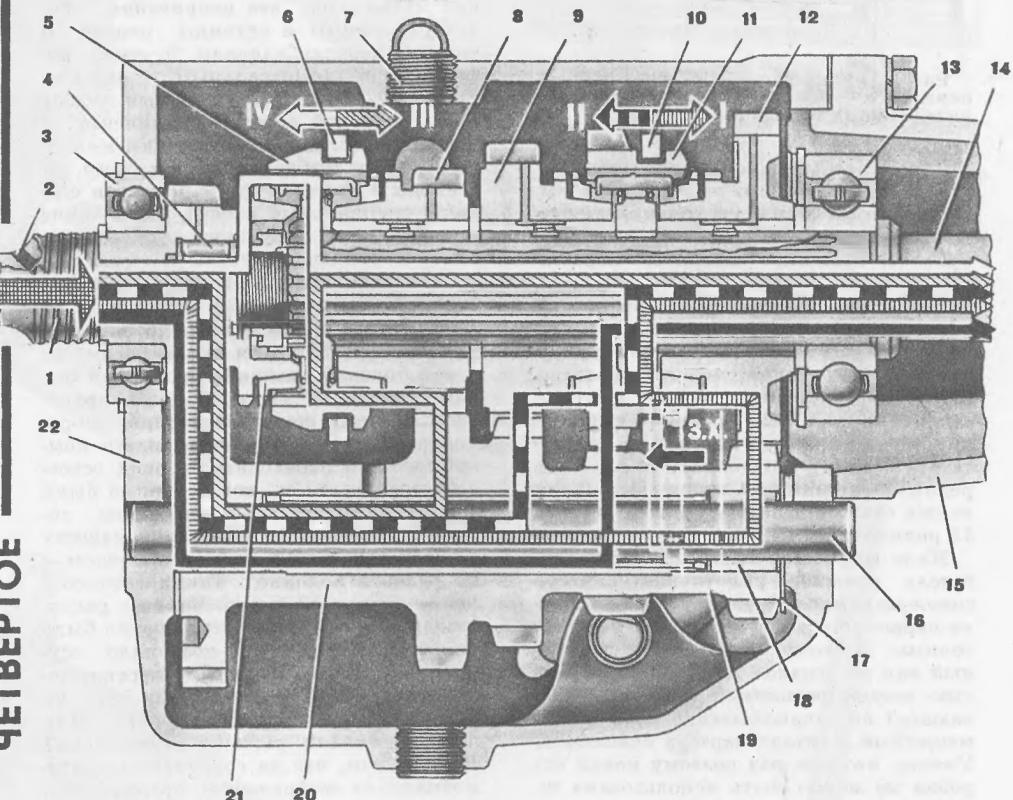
Устройство новой коробки передач: 1 — первичный вал; 2 — вентиляционное отверстие; 3 — подшипник первичного вала; 4 — роликовый подшипник; 5 — муфта синхронизатора; 6 — вилка; 7 — пробка горловины коробки; 8 — шестерня III передачи; 9 — шестерня II передачи; 10 — вилка; 11 — шестерня заднего хода со ступицей; 12 — шестерня I передачи; 13 — подшипник вторичного вала; 14 — вторичный вал; 15 — корпус удлинителя; 16 — ось блока шестерен; 17 — стальная упорная шайба; 18 — игольчатый подшипник промежуточного вала; 19 — картека заднего хода; 20 — блок шестерен промежуточного вала; 21 — ступица синхронизатора III и IV передач; 22 — картер коробки передач.
